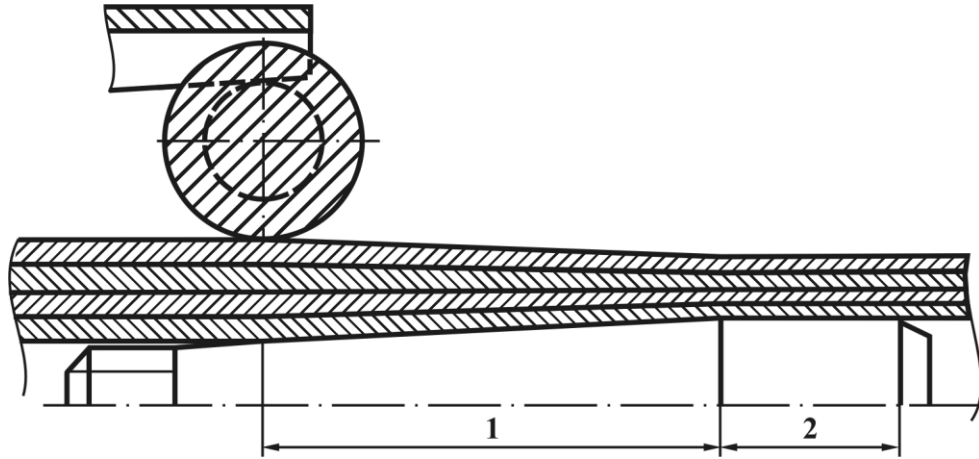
Схема способу пакетної прокатки багатошарової труби на оправці зі зворотною конусністю: 1 – зона обтиснення стінки; 2 – зона калібрування
